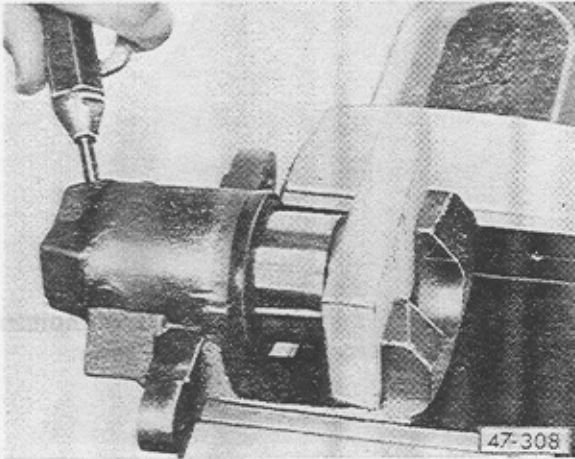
Kolben mit Druckluft aus dem Zylinder drücken
